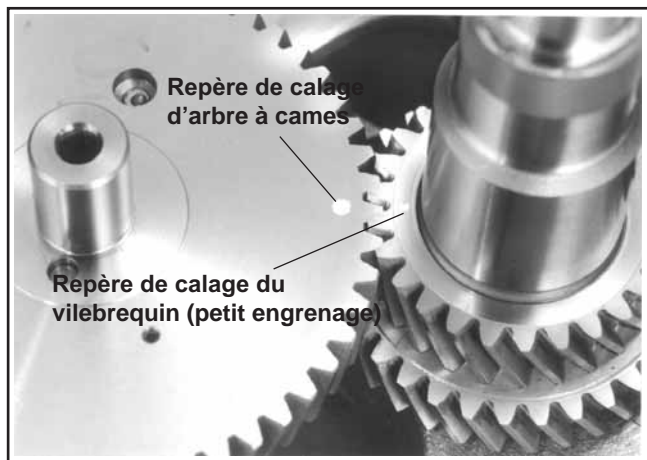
Alignement des repères de calage sur l'engrenage à cames et le réducteur à cames.
